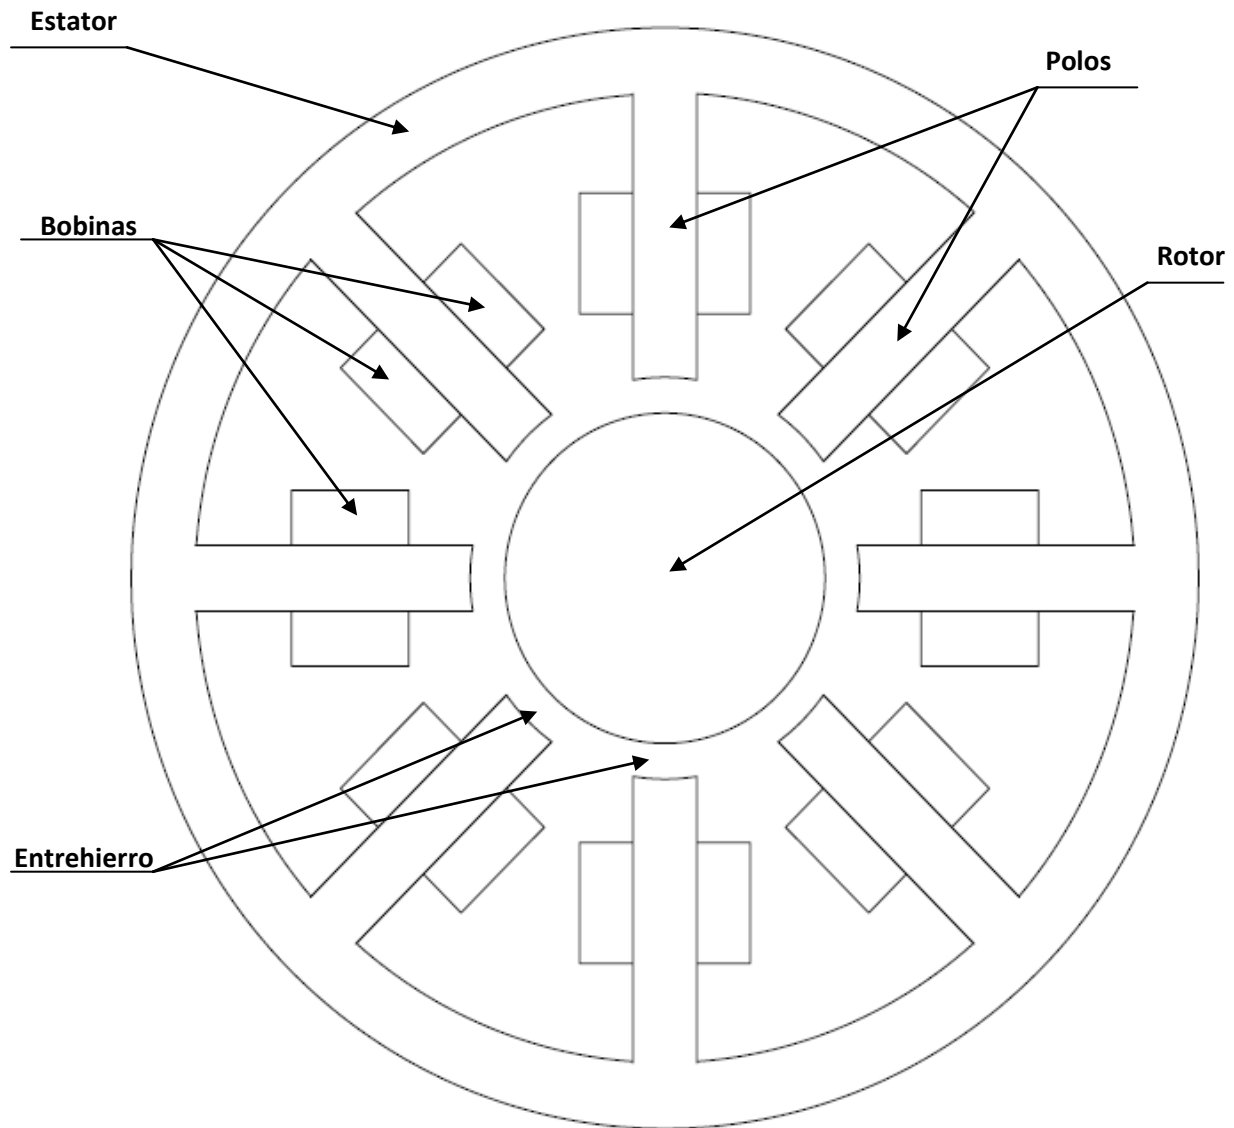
Esquema de partes principales del rodamiento electromagnético a diseñar.
